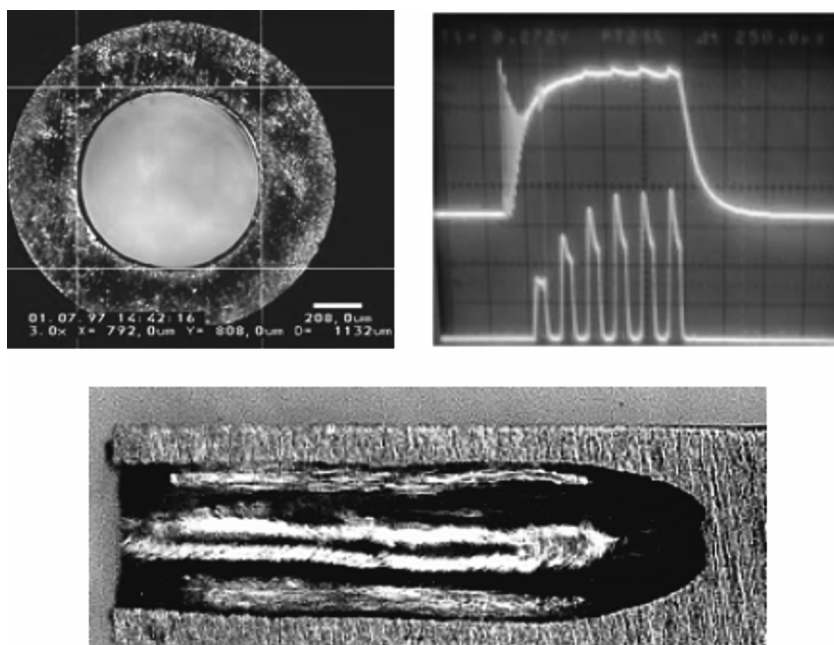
Одноимпульсное сверление отверстий в торце тонкой офтальмологической иглы из нержавеющей стали
